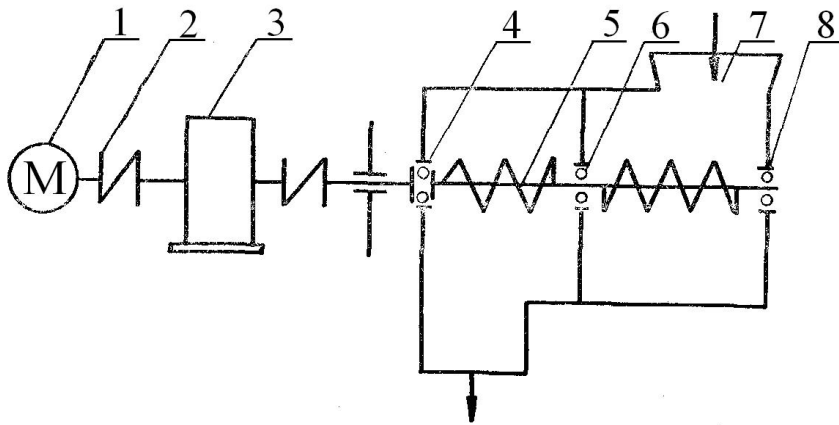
Схема гвинтового конвеєра: 1 – електродвигун; 2 – муфта; 3 – редуктор; 4 – вальниця кочення упорна головна; 5 – вал з гвинтом; 6 – вальниця проміжна; 7 – завантажувальний патрубок; 8 – вальниця задня
